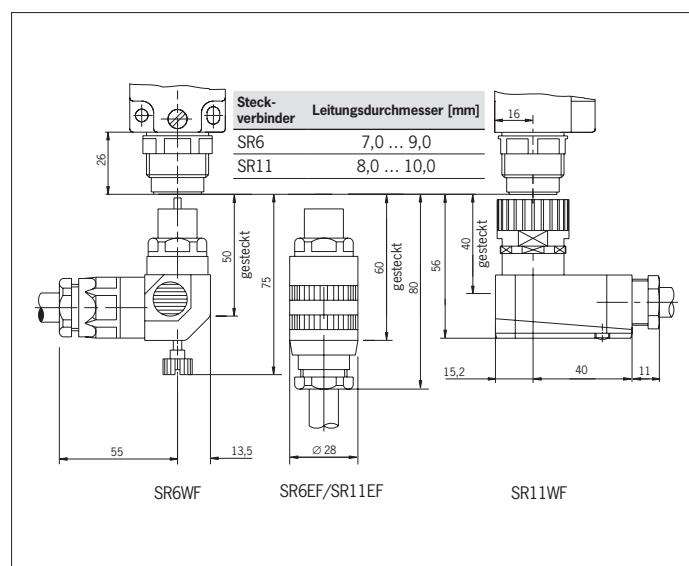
Maßzeichnung NZ2... mit Steckverbinder
